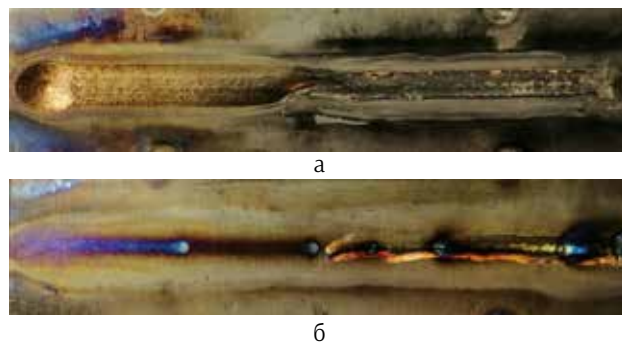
Фото лицевой и корневой стороны шва после сварки по слою флюса вольфрамовым электродом, справа – участок, предварительно покрытый флюсом, слева – участок чистого титана: а – лицевая сторона; б – корневая сторона
